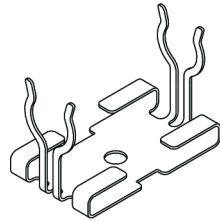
Montageclip (Befestigung mit M4-Schraube oder Kabelbinder)
